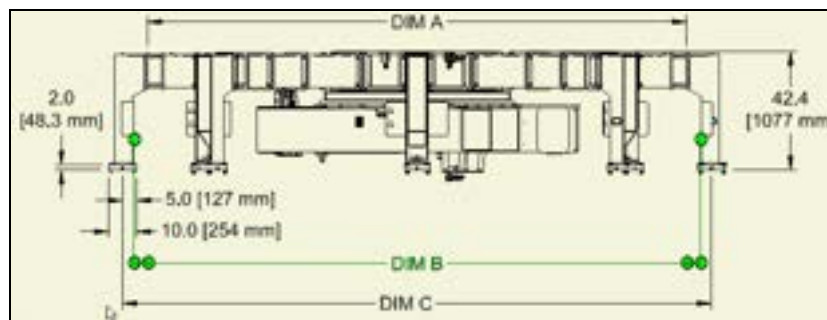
DIMENSIONS DE LA JAMBE DE SERRAGE DE
